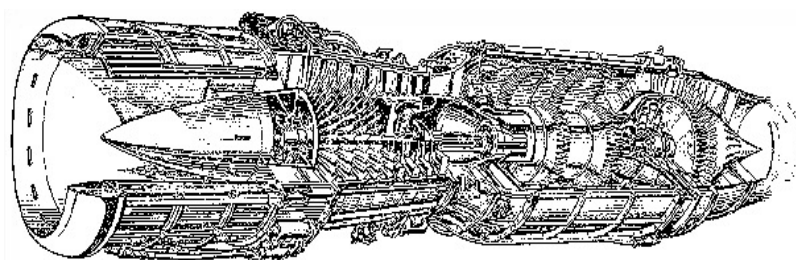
Patentovaný proudový motor anglický - F. Whittle [8]
